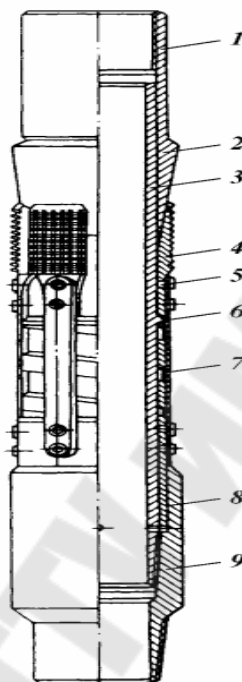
Клиновое подвесное устройство гидравлического действия: 1 – обсадная труба; 2 – конусообразная муфта; 3 – корпус; 4, 7 – верхнее и нижнее кольца центратора; 5 – штифт; 6 – пружинная планка центратора; 8 – поршень; 9 – соединительная муфта
